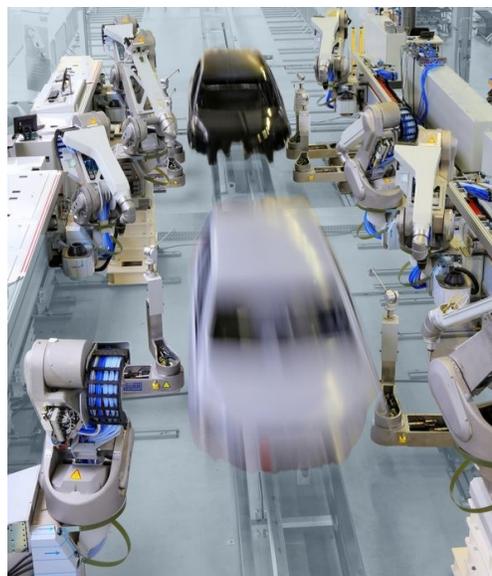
Der Prototyp in Aktion - Fördertechnik mittels mobilem Endgerät gesteuert
